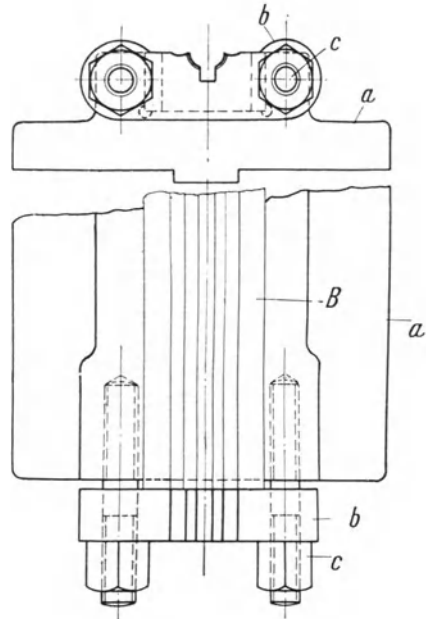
Das Fräsen der Spannuten in den Gewindebacken nach Abb. 529.
